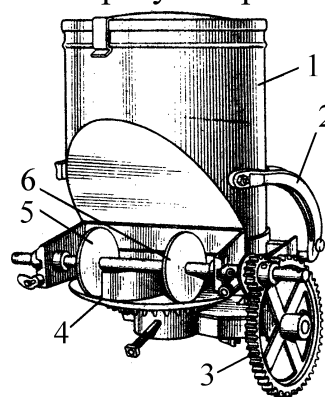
Туковывсевающий аппарат: 1 – бункер; 2 – регулятор высева; 3 – зубчатая передача; 4 – вращающаяся тарелка; 5, 6 – дисковые сбрасыватели
